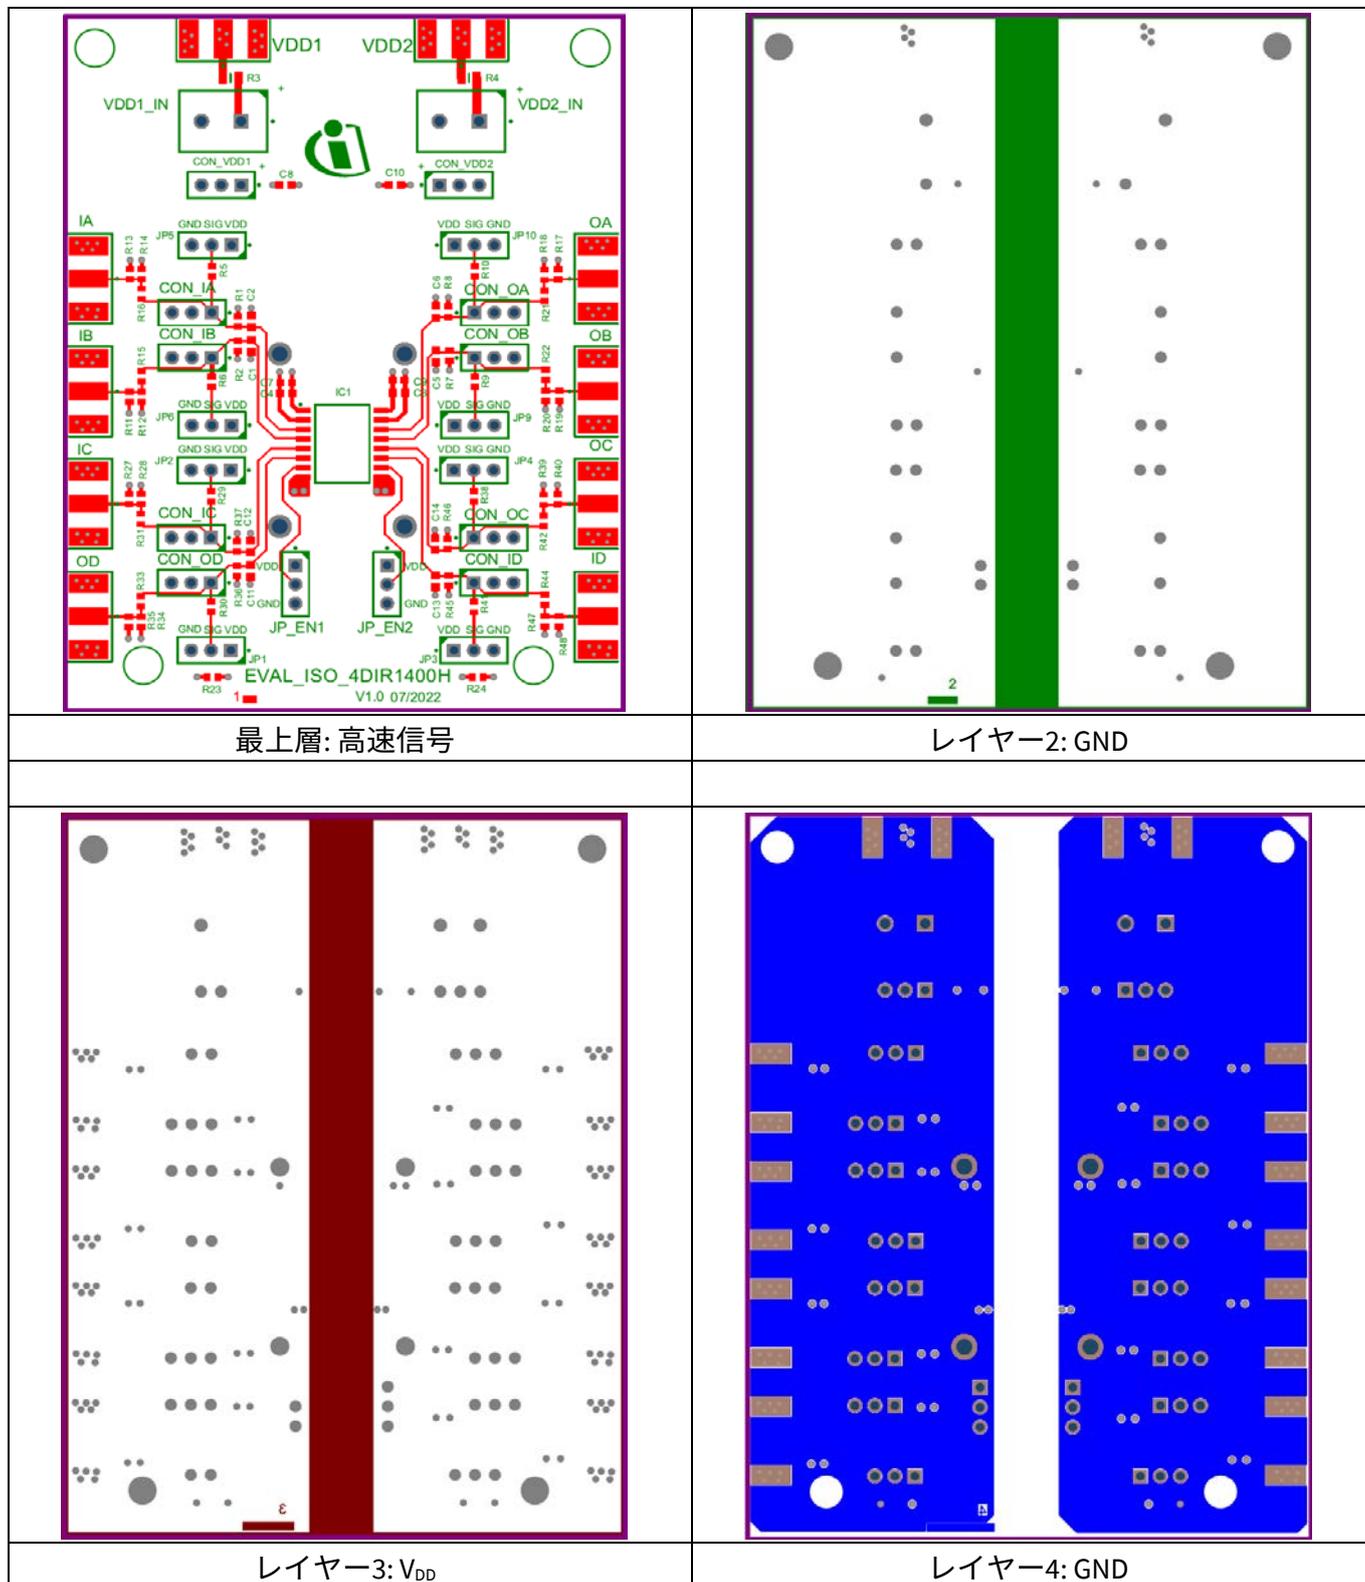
EVAL\_ISO\_4DIR1400H の PCB レイアウト
